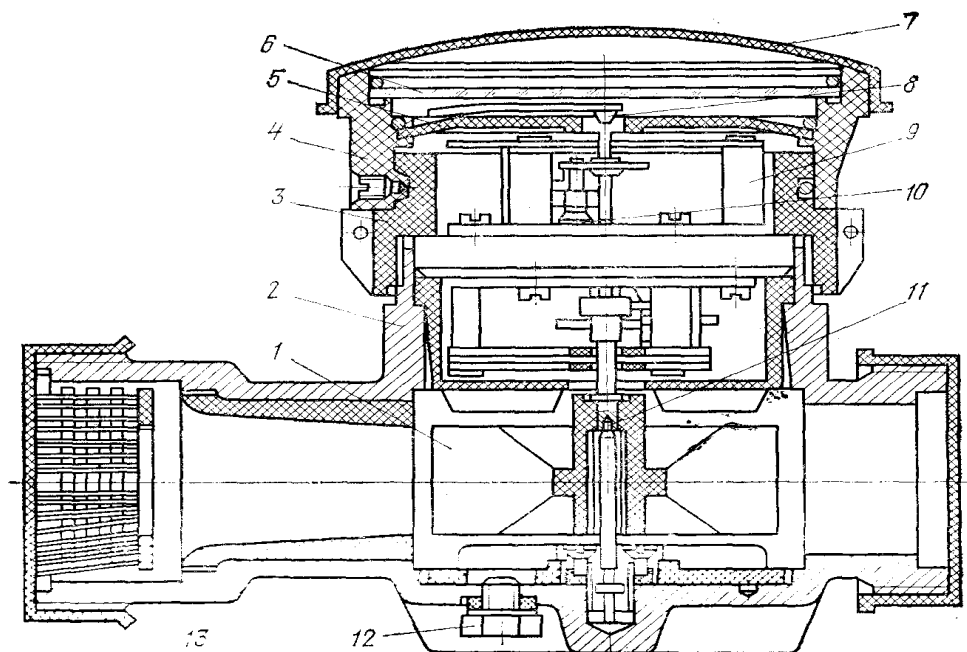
Дозатор воды ДВК.-40: 1 — крыльчатка; 2 — корпус; 3 — гайка; 4 — поворотная головка; 5 — циферблат; 6 — стекло; 7 — колпак; 8 — стрелка; 9 — счетная головка; 10 — магнитная муфта; 11 — точечная опора; 12 — пробка; 13 — фильтр
